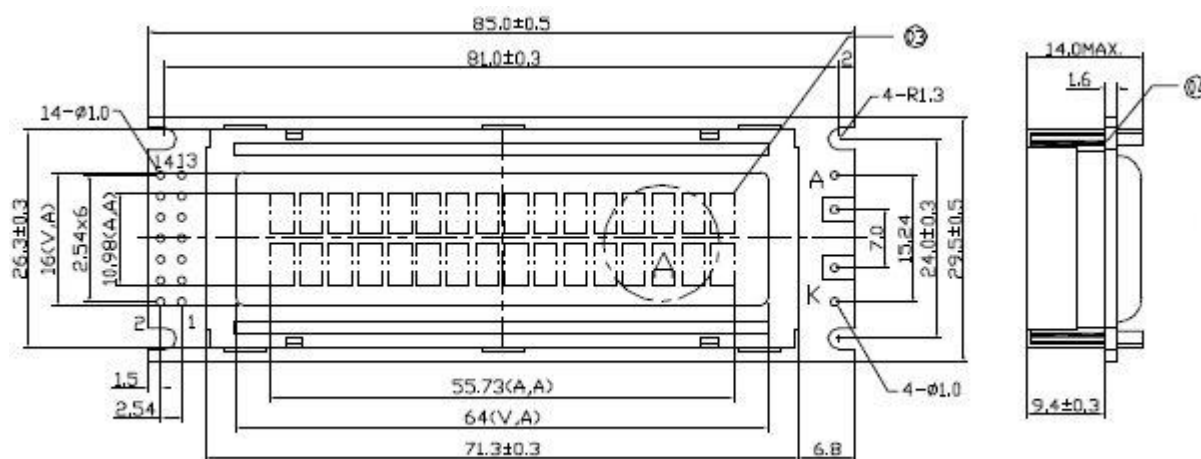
Присоединительные и габаритные размеры ЖКИ DV16230S2F.
